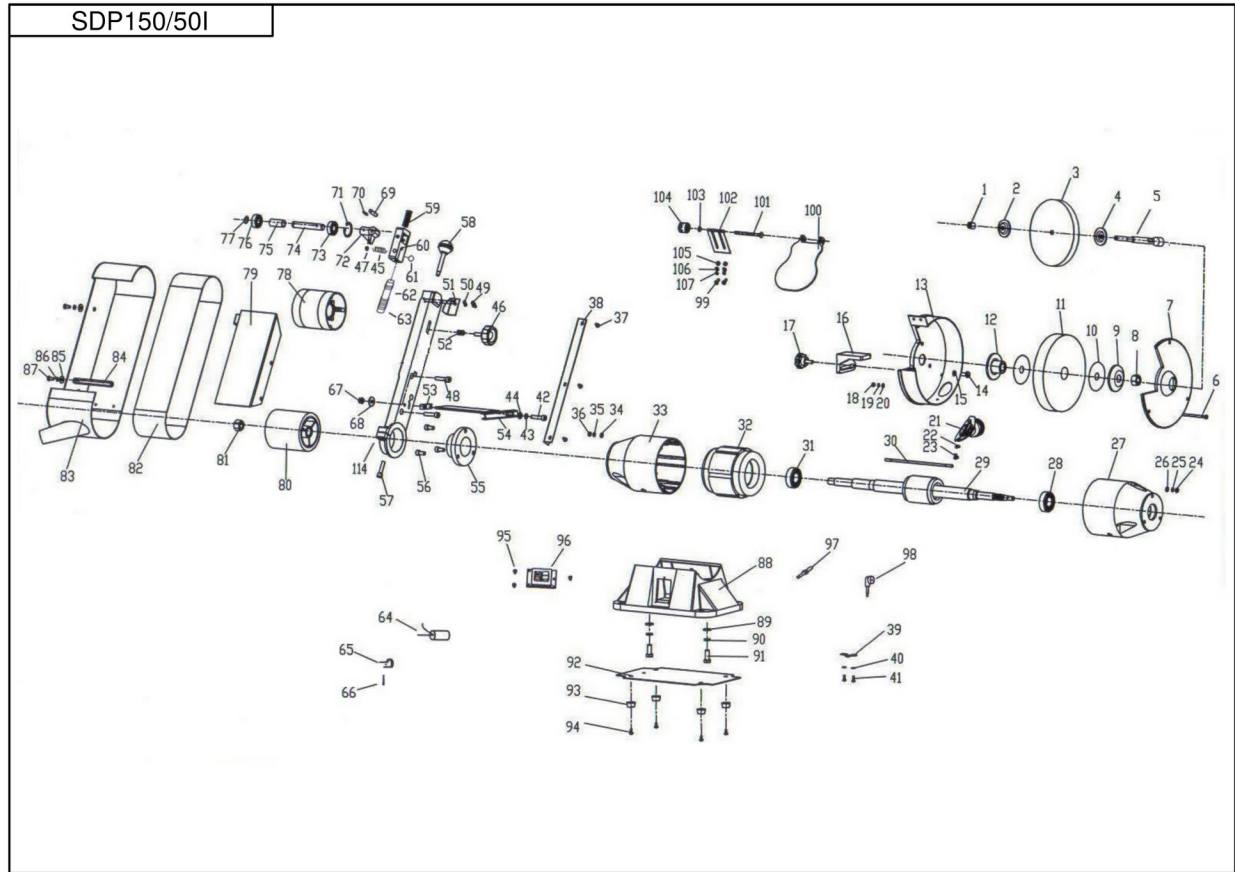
Vue éclatée de l'AY-150 IND LJ
